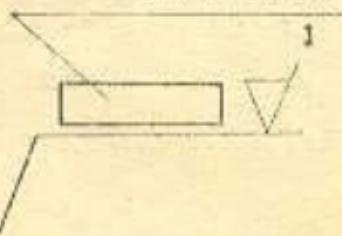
Обозначение шероховатости обработанной поверхности сварного соединения
